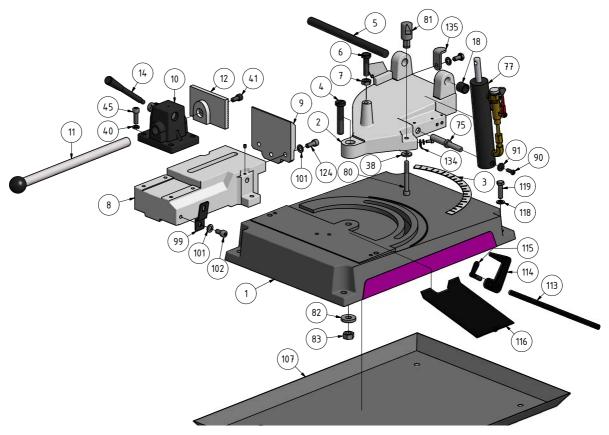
Ersatzteilzeichnung 3 von 4 - Parts drawing 3 of 4
